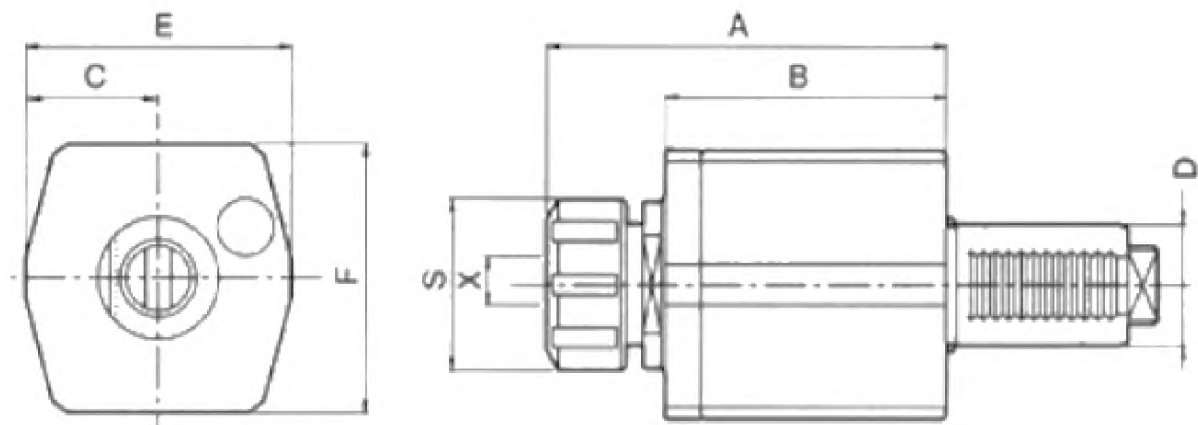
Осьова свердлильно-фрезерна головка DA20180916
